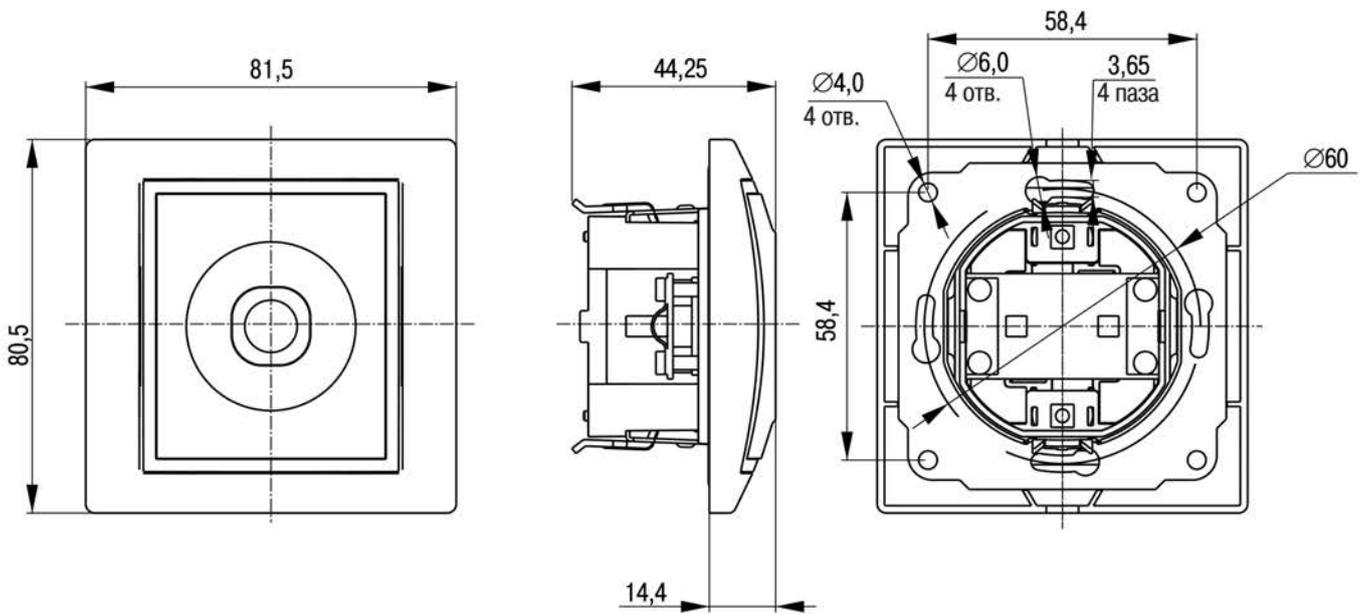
Габаритные и присоединительные размеры РТВ11-КБ, РТВ11-ККм
